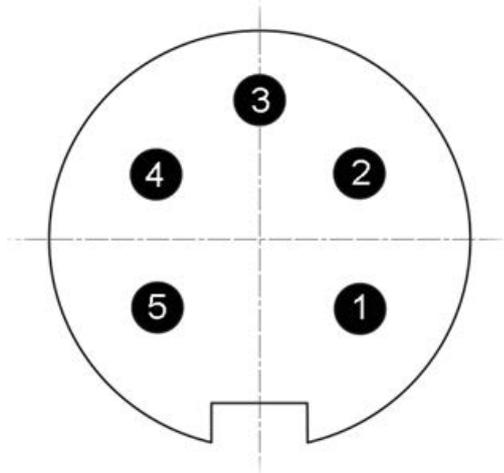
Vue d'ensemble du brochage du connecteur d'entrée
